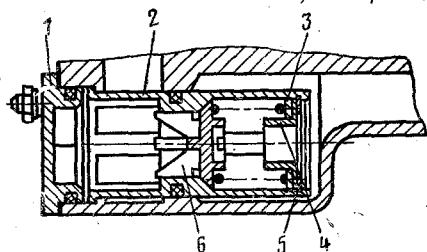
Редукционный клапан верхнего масляного агрегата:
